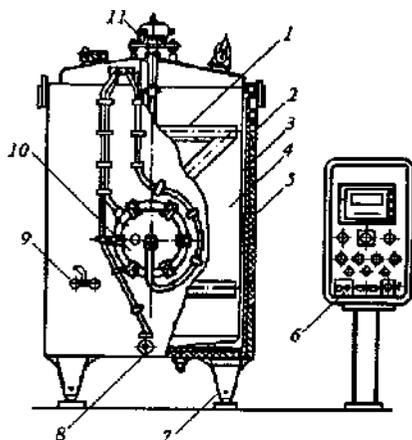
Резервуар для приготовления кисломолочных продуктов: 1 - мешалка; 2 - теплоизоляция; 3 - теплообменная рубашка; 4 - внутренний корпус; 5 - наружный корпус; 6 - пульт управления; 7 - ножки; 8 - патрубок заполнения-опорожнения; 9 - пробоотборный кран; 10 - люк; 11 - привод мешалки
